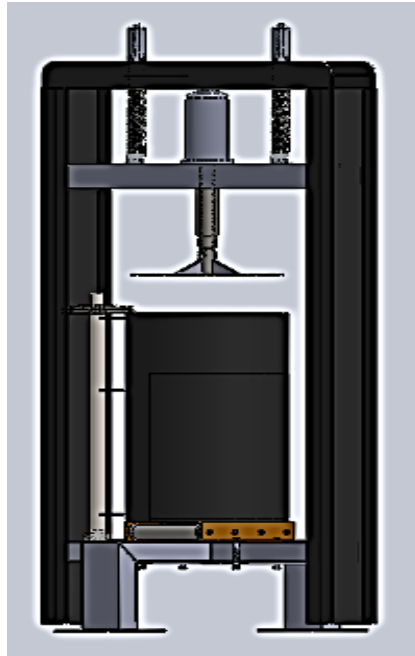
Diseño en 3D de la máquina compactadora de ensilaje
